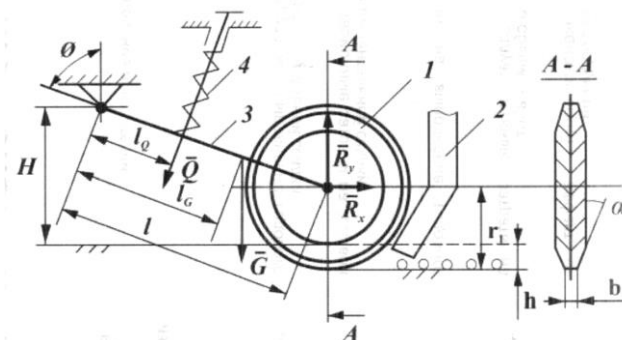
Схема сил, що діють на бороздоутворюючу будову: 1 – бороздоутворюючі накладки, 2 – напрямник насіння, 3 – повідець, 4 – натискна штанга з пружиною.
